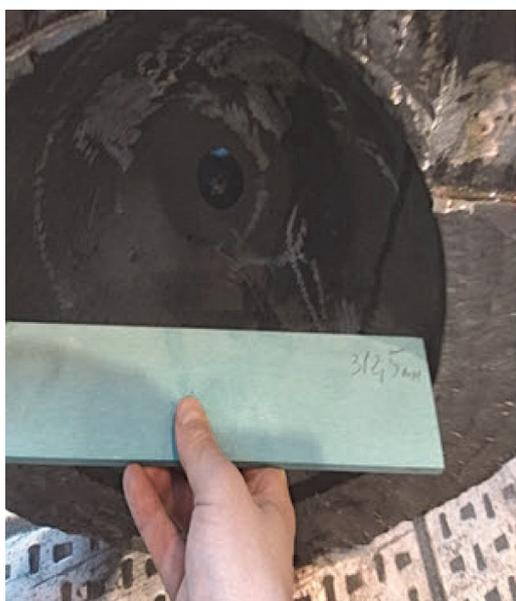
Крышка (боковые прибыли установлены по боковой поверхности фланцев)
